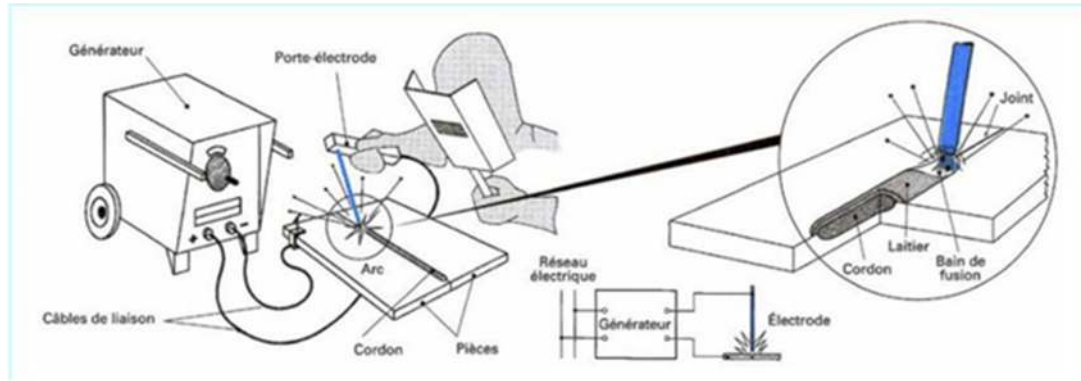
principe de soudage à l'électrode enrobée
